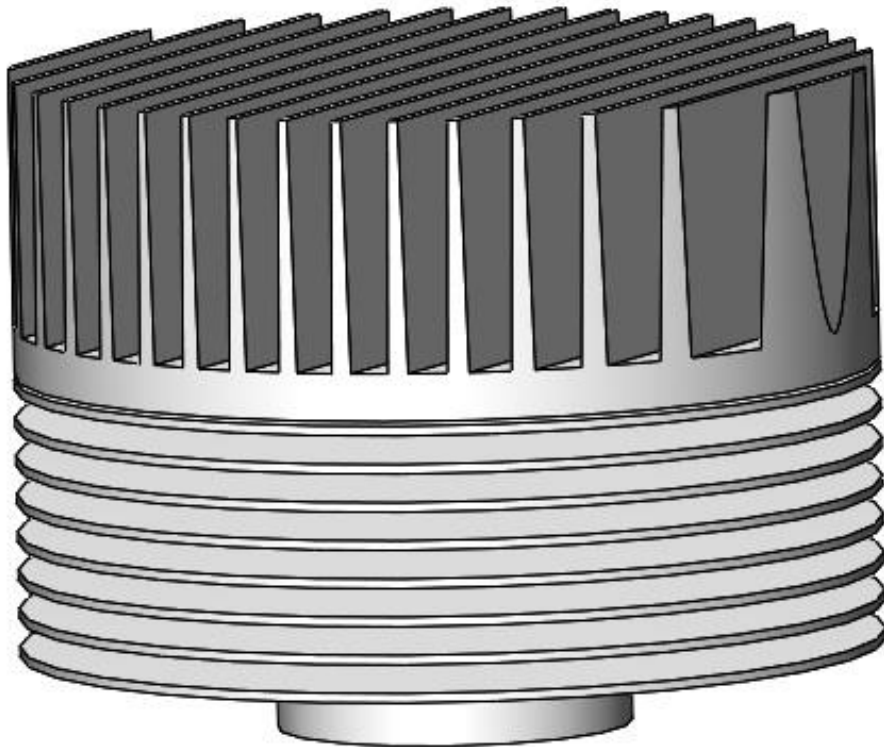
Model motoru dle skutečných rozměrů a zaoblení
